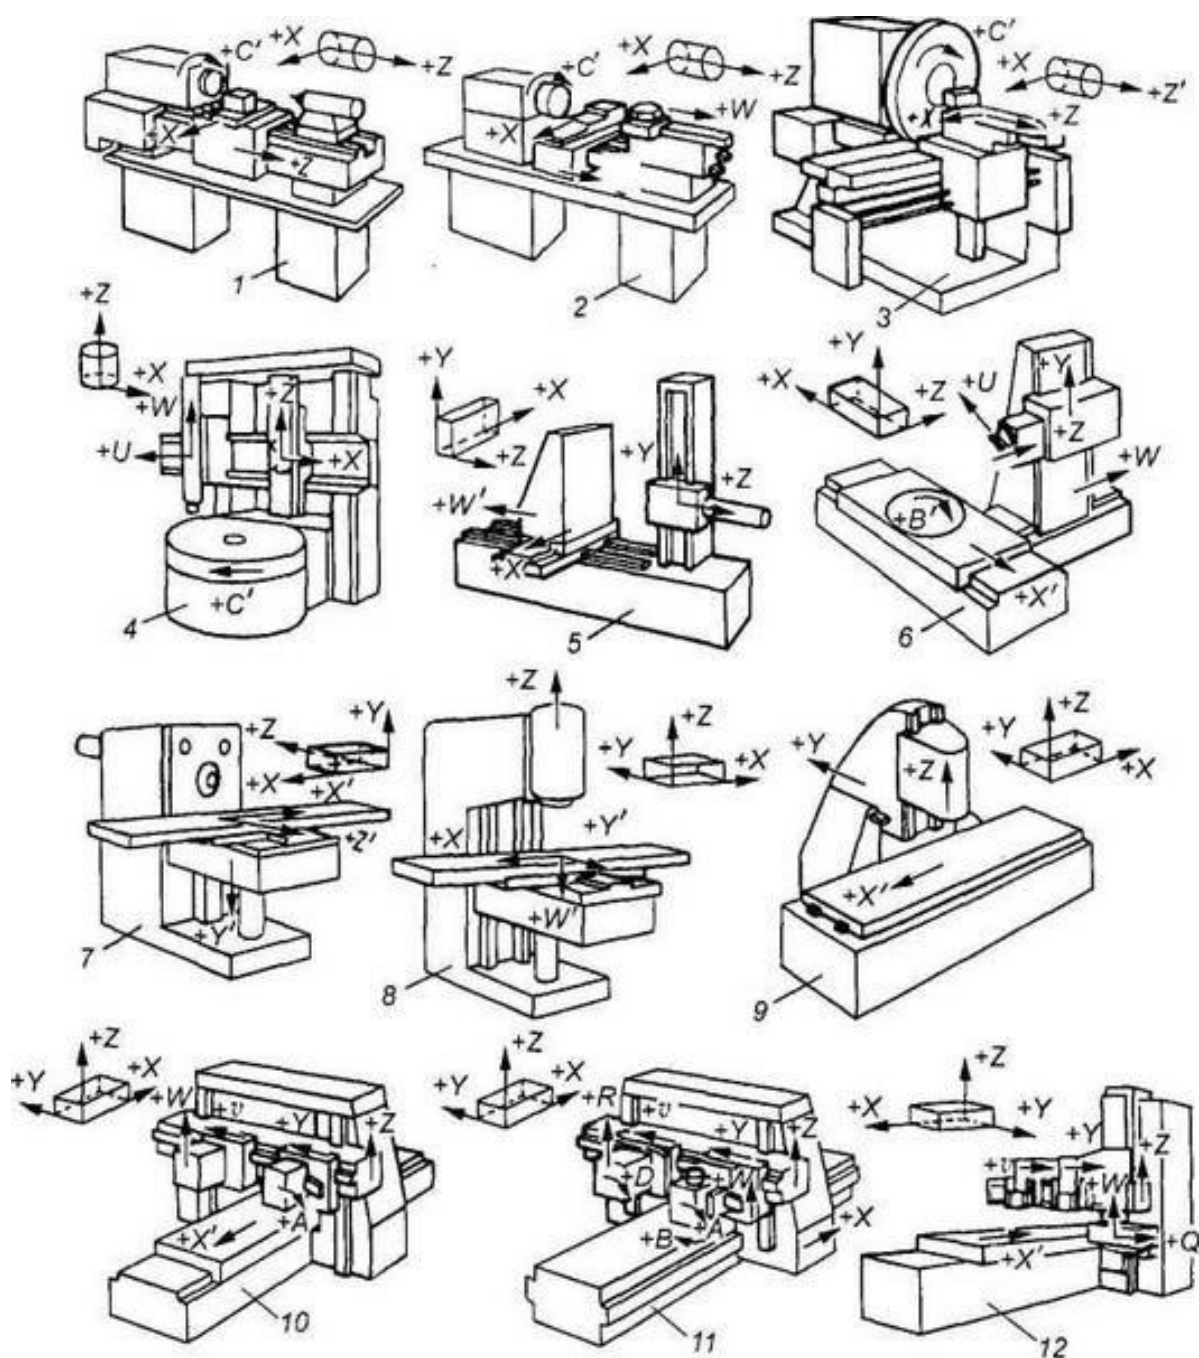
Позначення осей координат і напрямків руху робочих органів в верстатах з ЧПК: 1 – токарно-гвинторізний; 2 – токарно-револьверний; 3 – лоботокарний; 4 – токарно-карусельний; 5, 6 – горизонтально-розточувальні; 7 – консольно-фрезерний горизонтальний; 8 – консольно-фрезерний вертикальний; 9 – поздовжньо-фрезерний вертикальний; 10 – поздовжньо-фрезерний двостійковий; 11 – поздовжньо-фрезерний з рухомим порталом; 12 – одностоечний поздовжньо-стругальний
